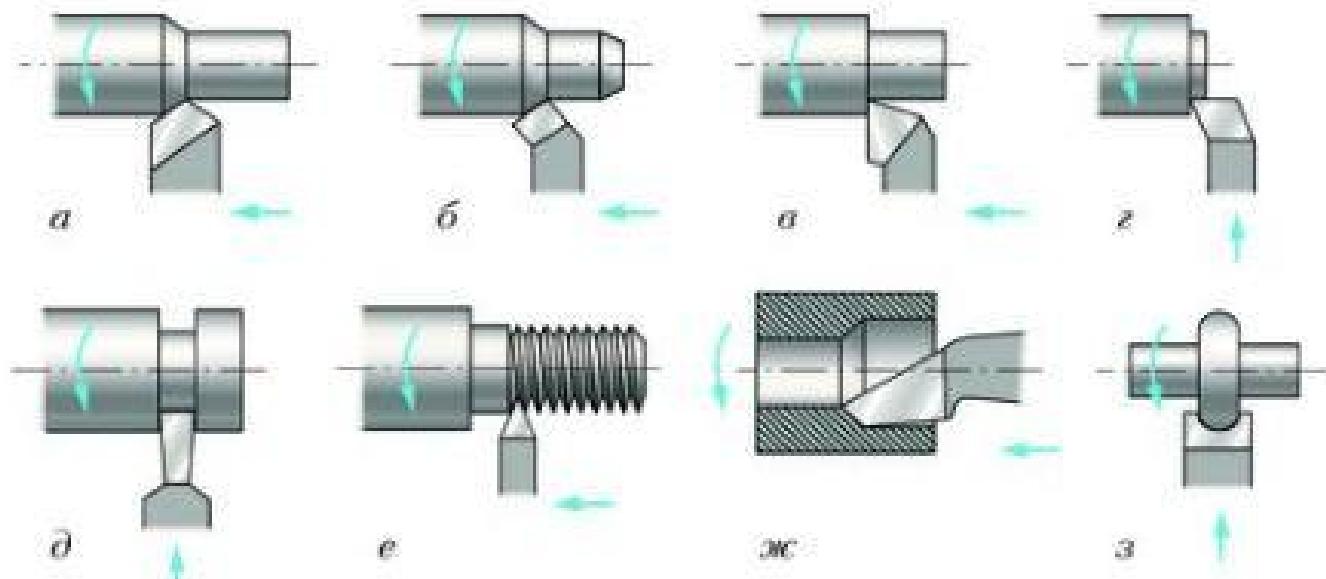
Токарные резцы: а – проходной прямой; б – проходной отогнутый; в – проходной упорный; г – подрезной; д – отрезной; е – резьбовой; ж – проходной расточной; з – фасонный
